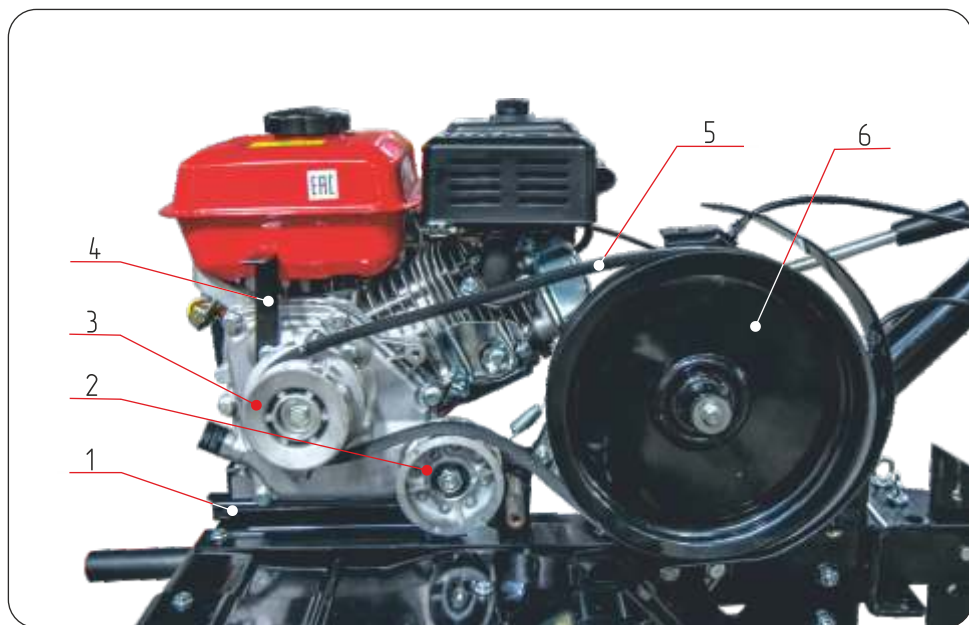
Мотоблок. Вид слева (защитный кожух снят)
